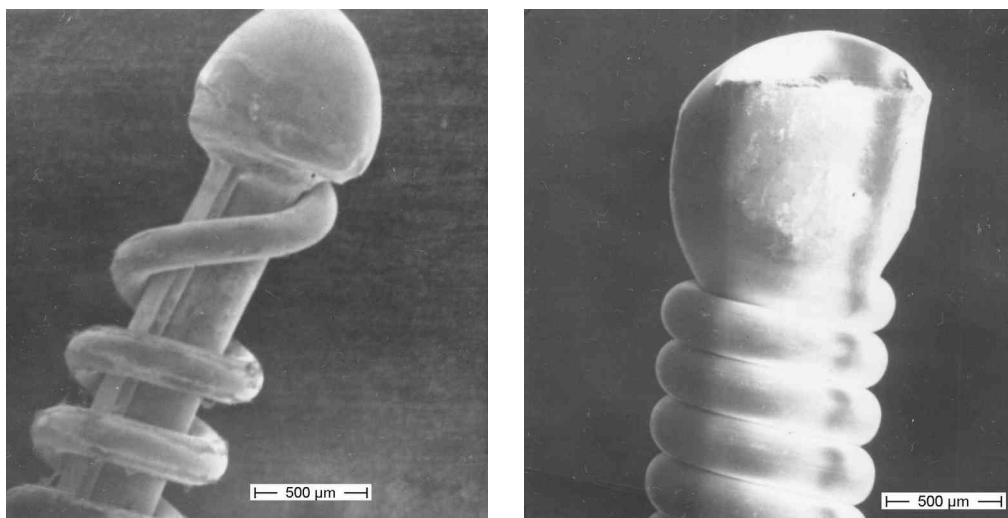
Herzkatheter-Führungsdrähte; Stützdraht und Hülldraht miteinander verschweißt. links Westmodell (Laserschweißung), rechts Ost-Versuchsmodell (Elektronenstrahlschweißung)
